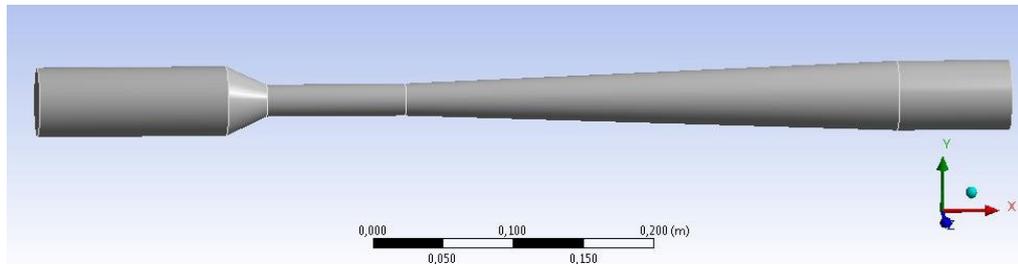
Venturi 2 - Comprimento da garganta 99 mm e Diâmetro da garganta 23 mm.
